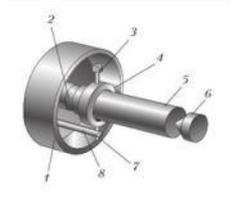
Установка заготовки с помощью поводковой планшайбы: 1 – корпус планшайбы; 2 – передний центр; 3 – створчатый винт; 4 – втулка; 5 – заготовка; 6 – задний центр; 7 – стержень; 8 – поводок
